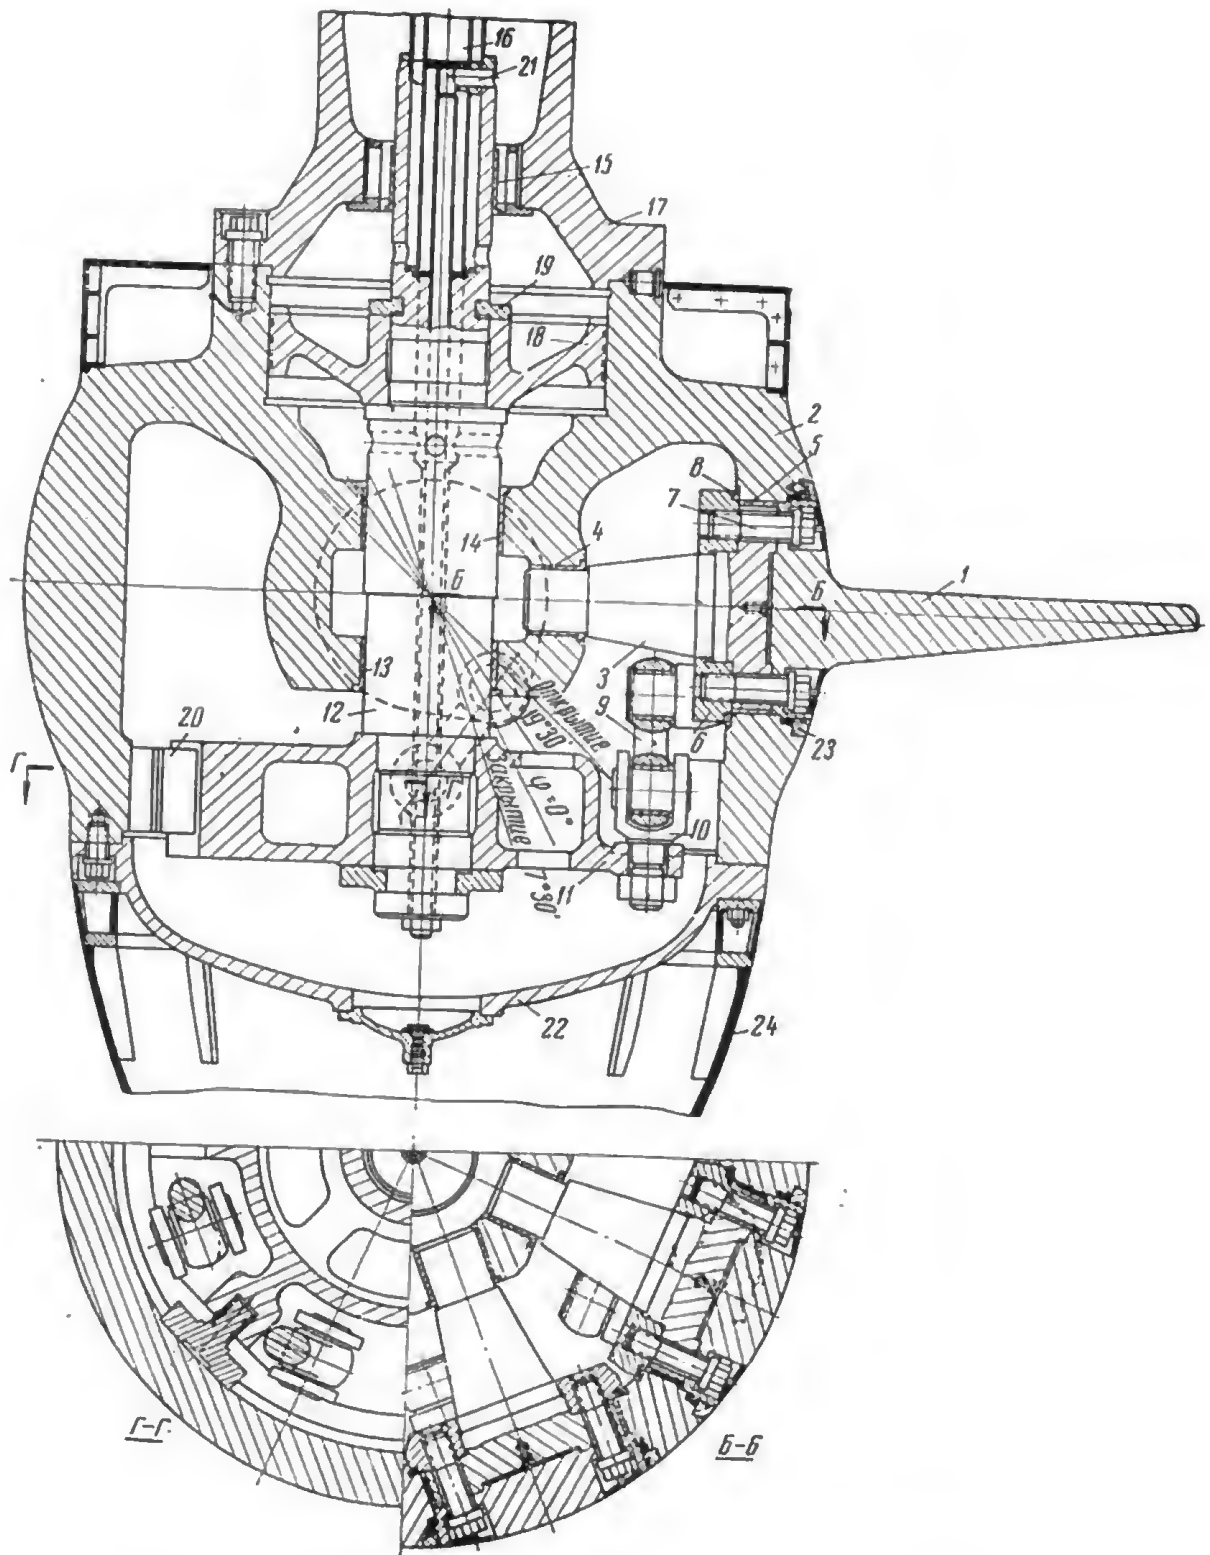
Рабочее колесо крестовинного типа поворотнолопастной турбины.
